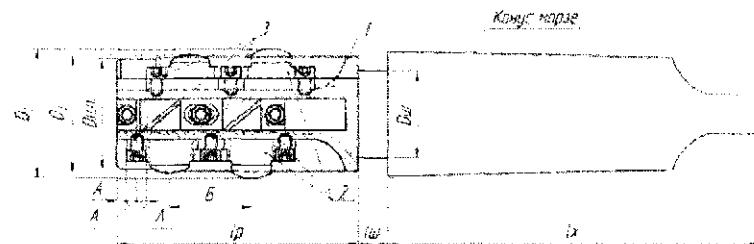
Общий вид резцовой сборной развертки со сдвоенными безвершинными зубьями с разными диаметрами
